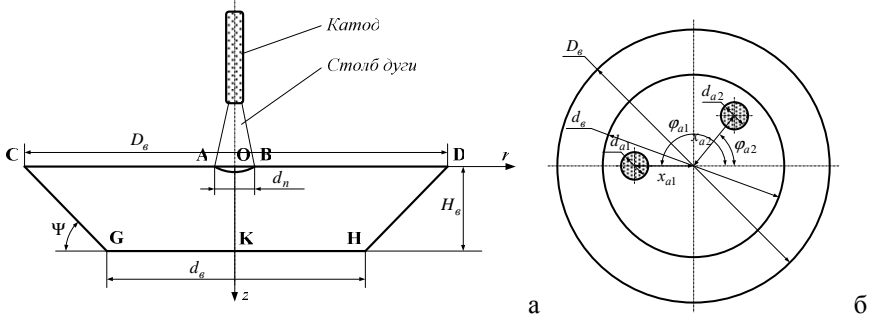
Основные размеры ванны: вид подины сбоку (а) и сверху (б):
